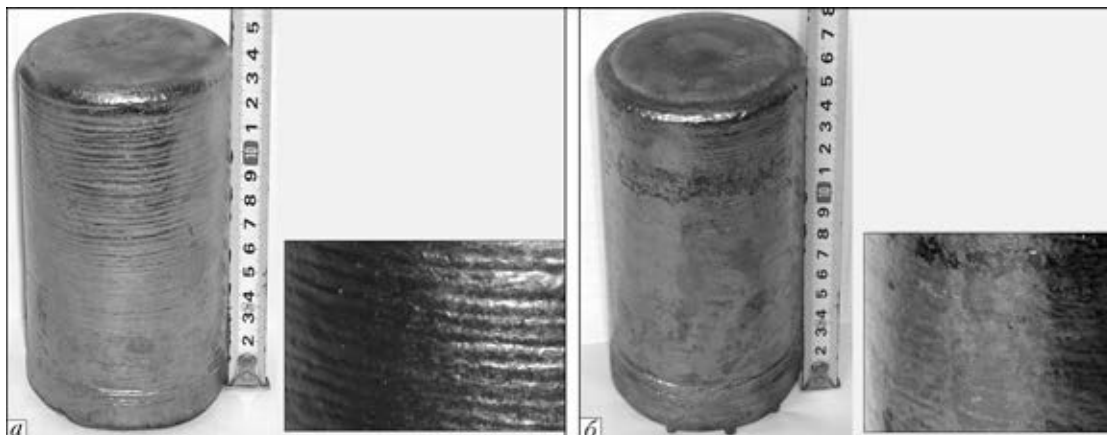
Внешний вид и боковая поверхность слитков титана, выплавленных с импульсным электропитанием: а — плавка № 825; б — плавка № 826
